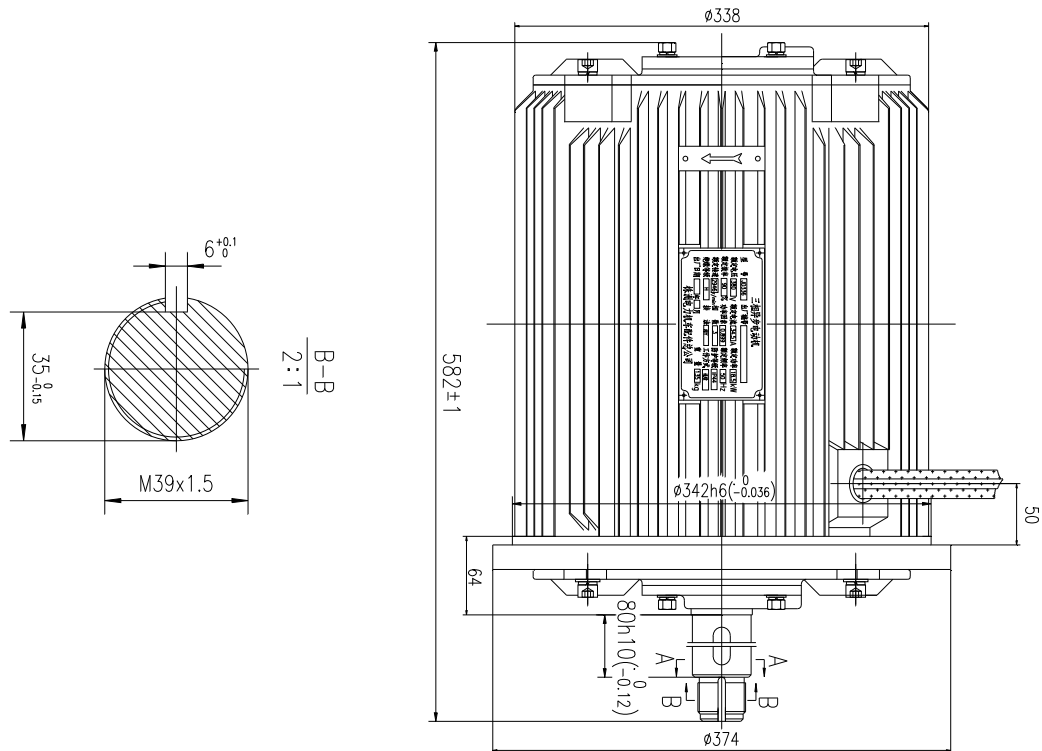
Схема внешнего вида двигателя JD336A и размеры установки
